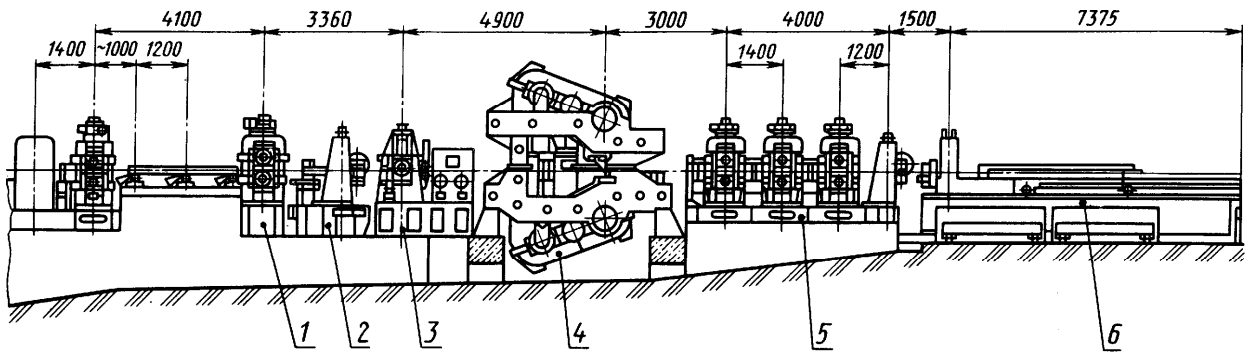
Схема расположения оборудования для высокочастотной сварки замкнутых холодогнутых профилей
